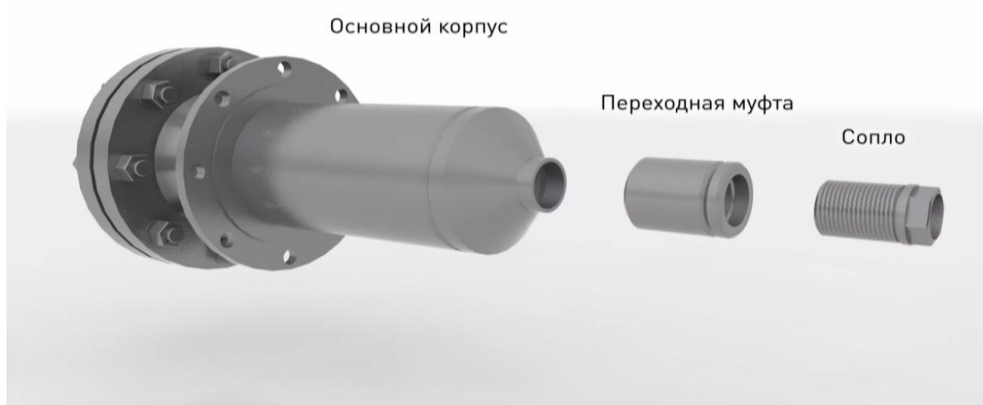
Конструкция приемной камеры эжекторного устройства
